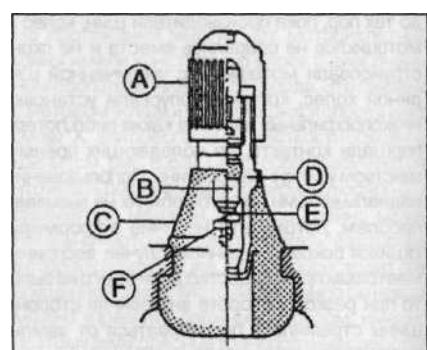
д Обрезиненный шинный вентиль в разрезе
